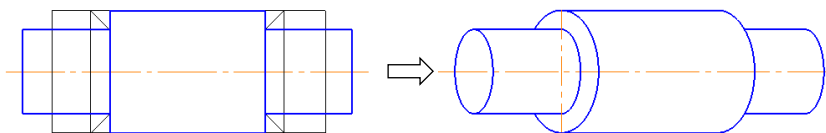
Схема получения двустороннего уступа для цилиндрических заготовок
